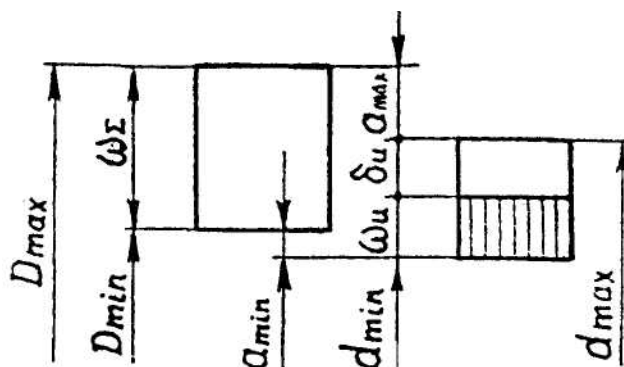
Схема образования суммарной погрешности обработки для диаметра отверстия, обработанного сверлением, зенкерованием и развёртыванием
